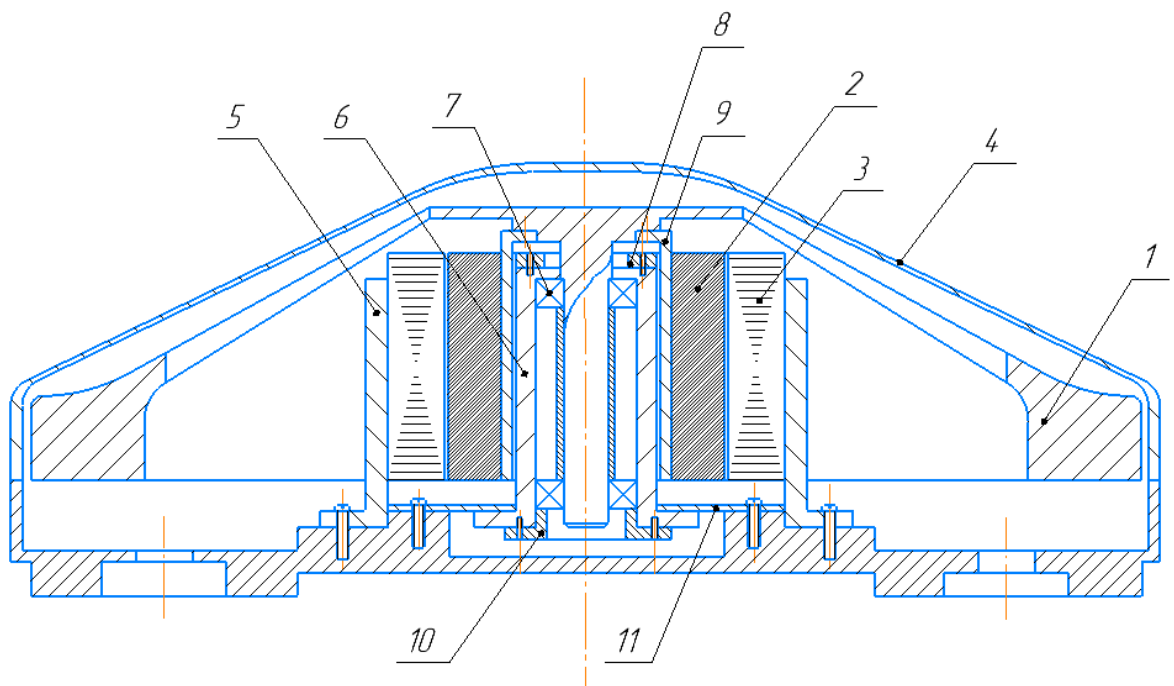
Сборочный чертеж электродвигатель-маховика
